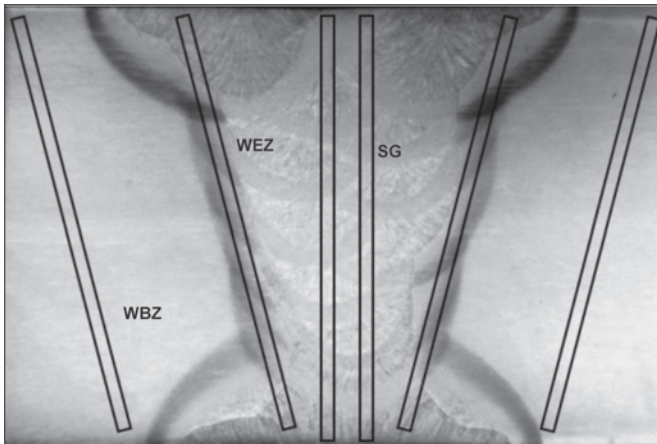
Probenlage im Schweißnahtgefüge S 890
